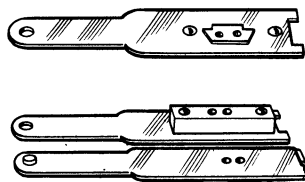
Приспособления для облегчения труда при сверлении определенных отверстий.
